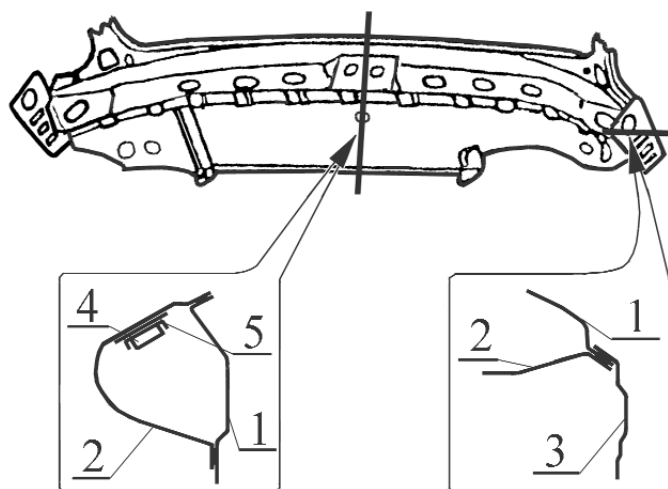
Детали панели задка с поперечиной в сборе 1119-5601080. Наименование входящих деталей и количество сварочных точек, которыми они соединяются с панелью задка, приведены в таблице 16.
